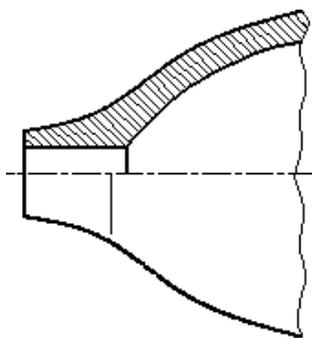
Образец оформления плавного перехода от одной поверхности к другой
